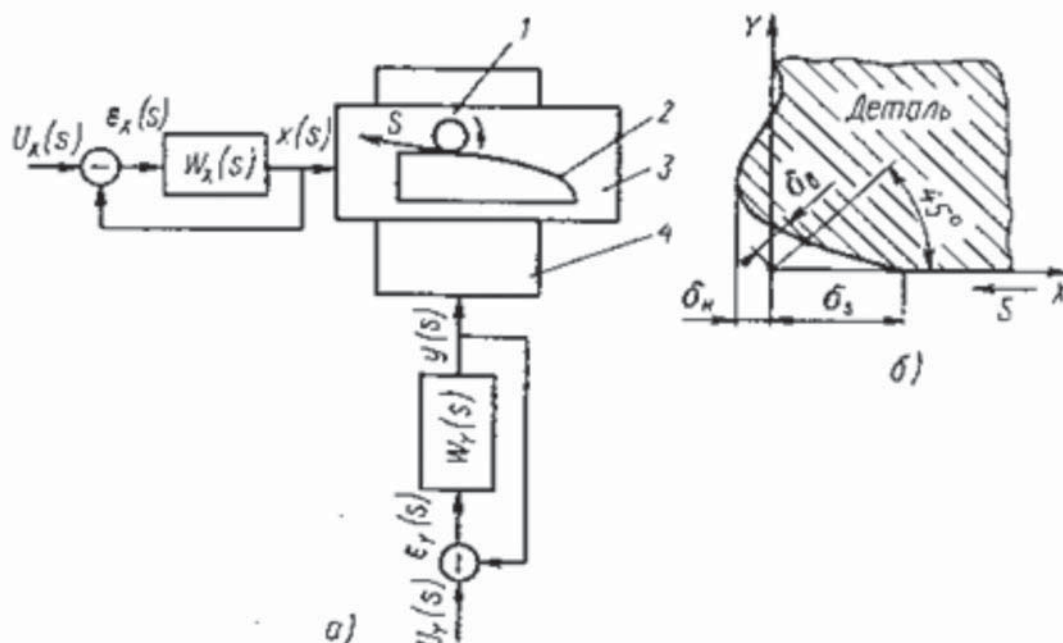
Схема двухкоординатного привода подачи фрезерного станка (а) и формирование погрешностей при обработке прямого угла (б): 1 - фреза; 2 - деталь; 3 - стол; 4 - салазки; S - подача по контуру
